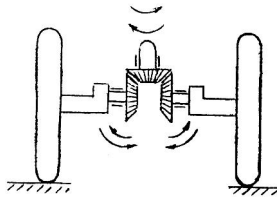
Схема зубчастого механізму самоустановлення нижнього станка
